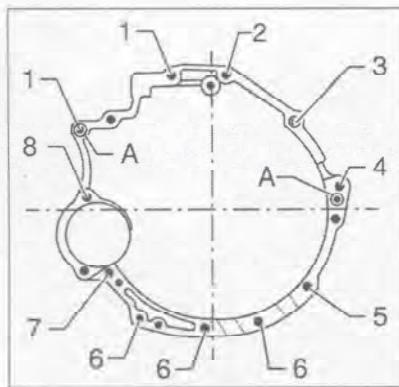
Последовательность затяжки болтов крепления коробки передач (автомобили с 6-цилиндровыми двигателями).
